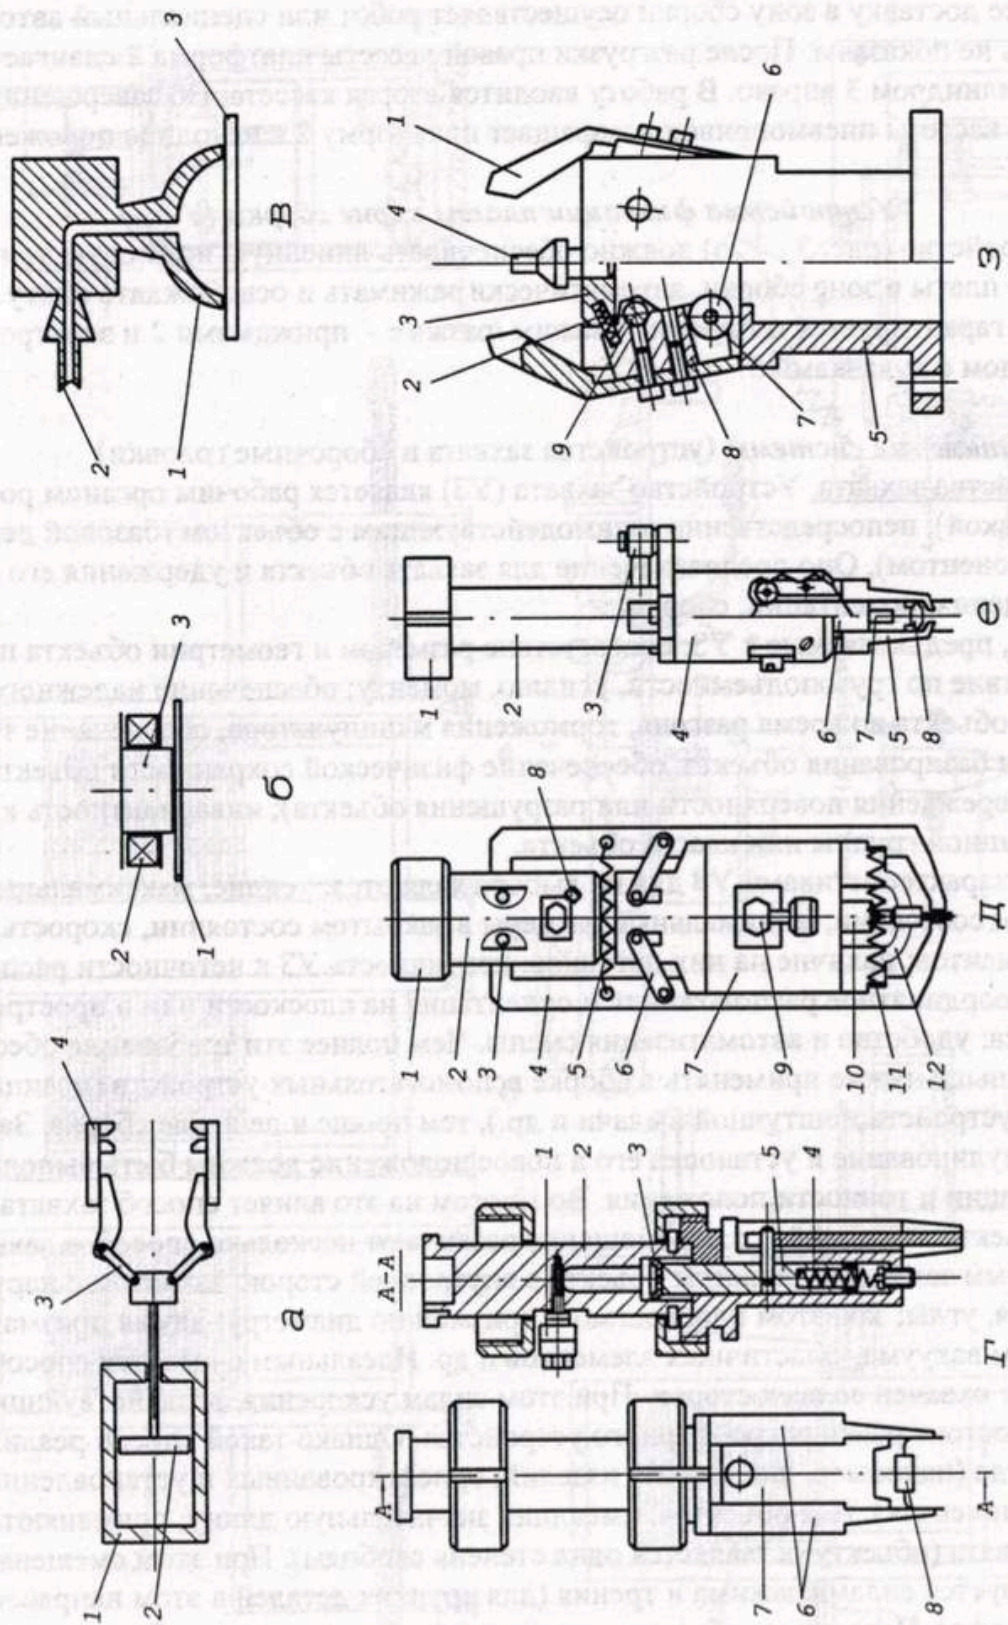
Захватные устройства (ЗУ) и сборочные головки (СГ)
